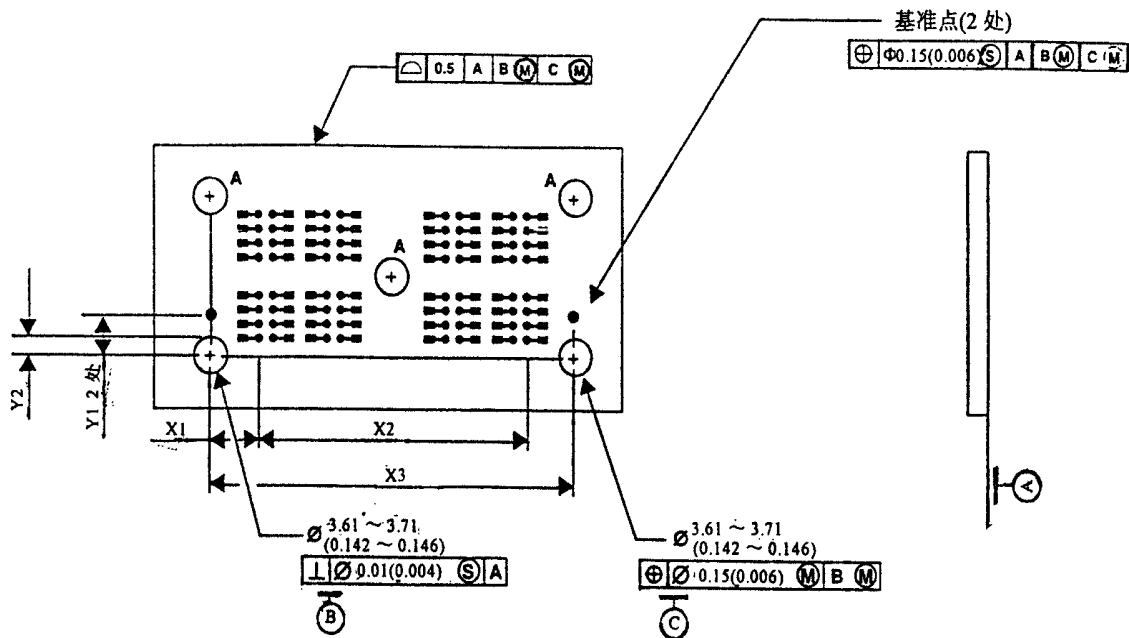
使用几何图形标注尺寸和公差的印制板加工图范例
